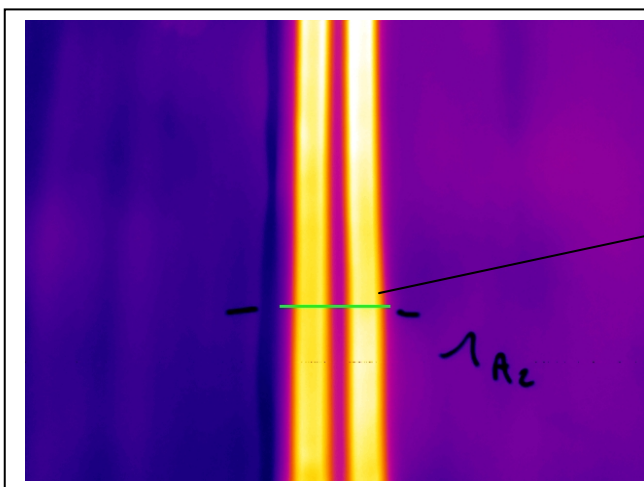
Vue IR d'une soudure 30 secondes après sa réalisation.
